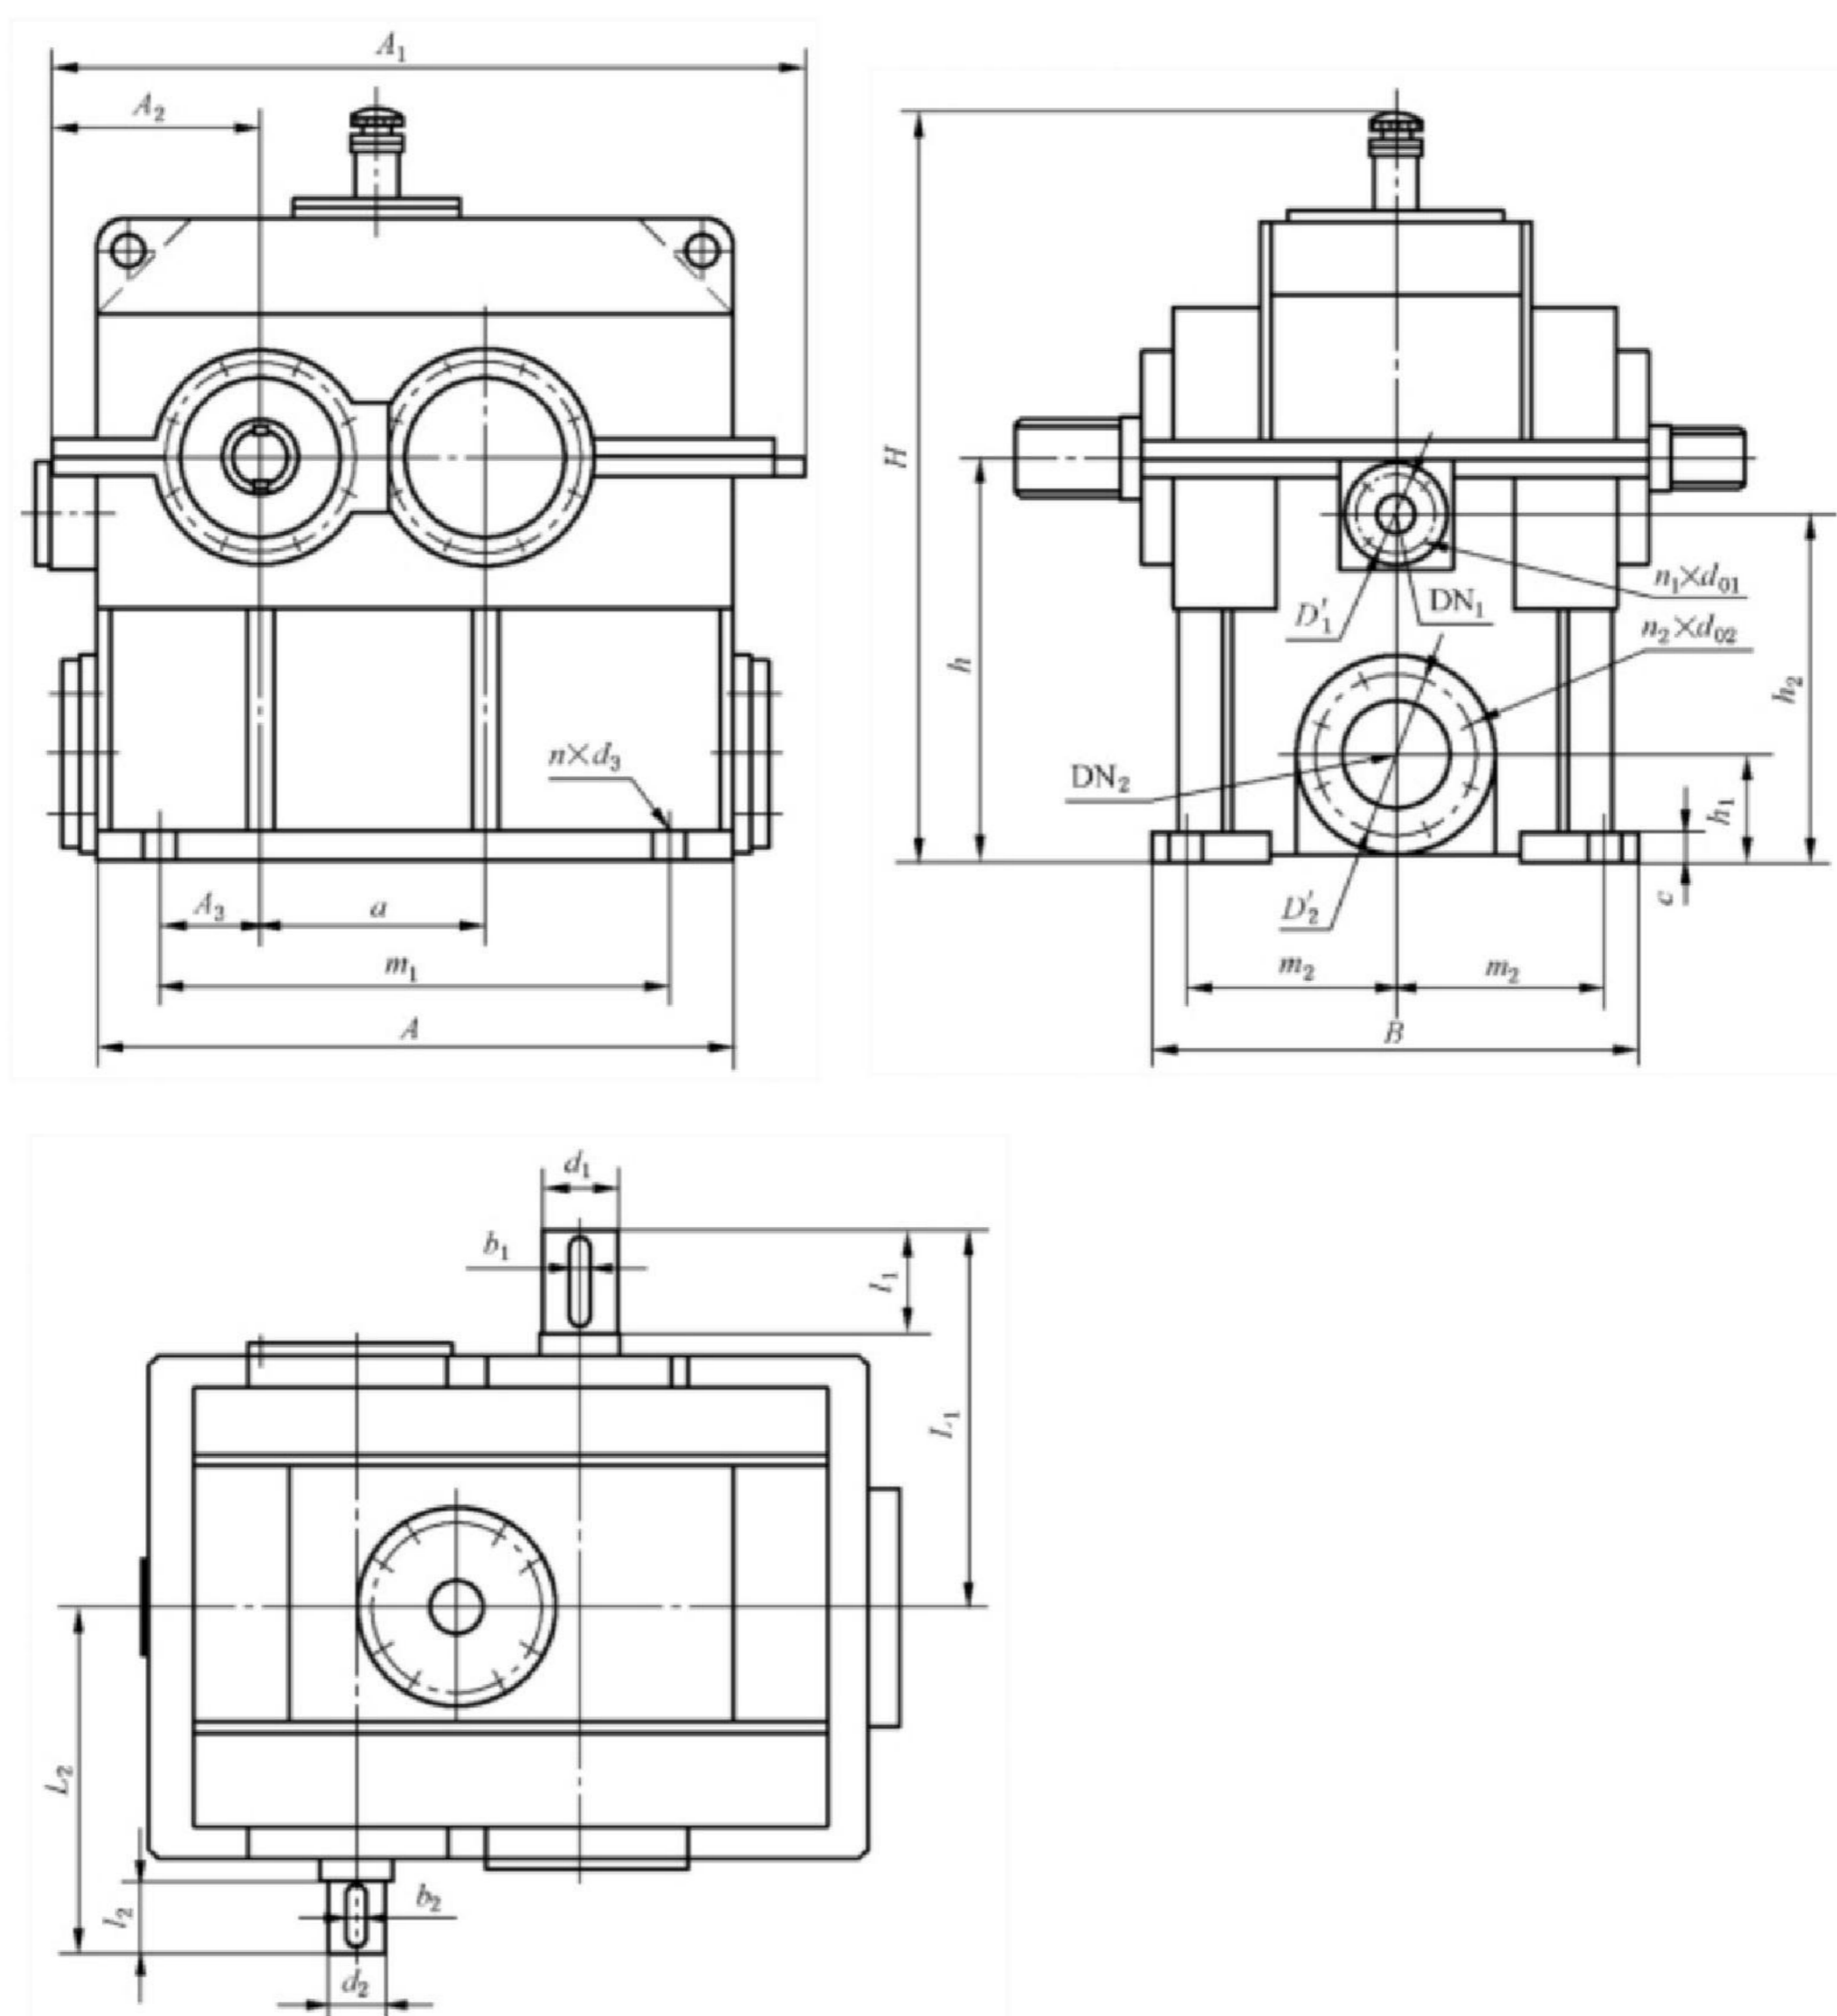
GS160~GS400 齿轮装置外形及连接尺寸
